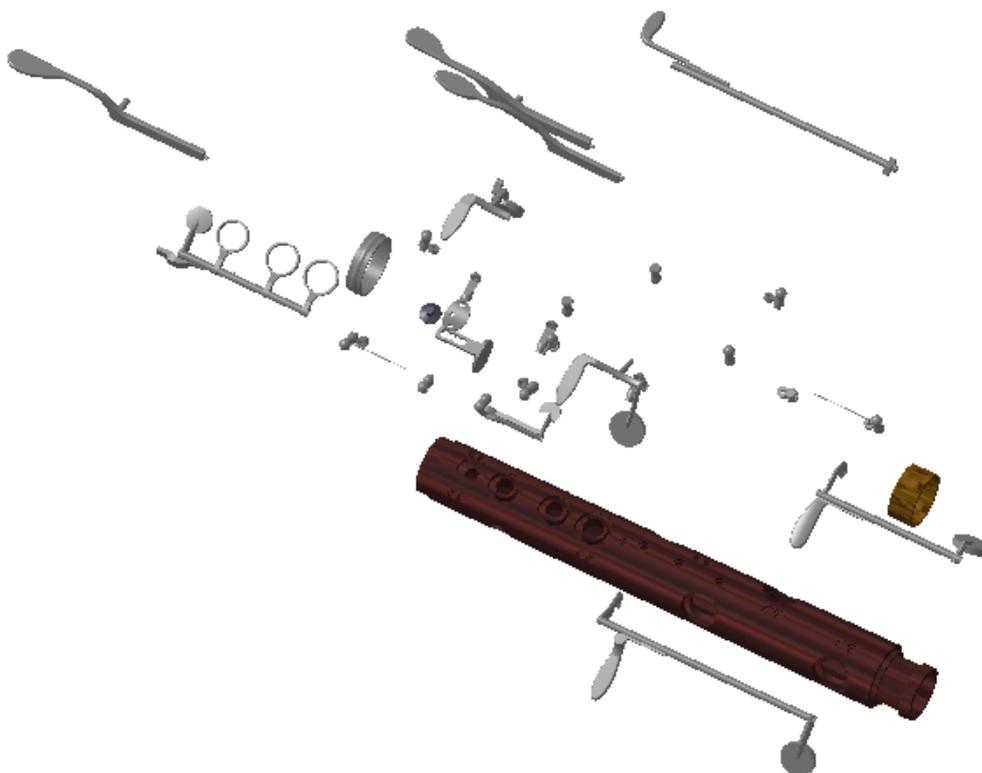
Vista explosionada del conjunto del cuerpo inferior
